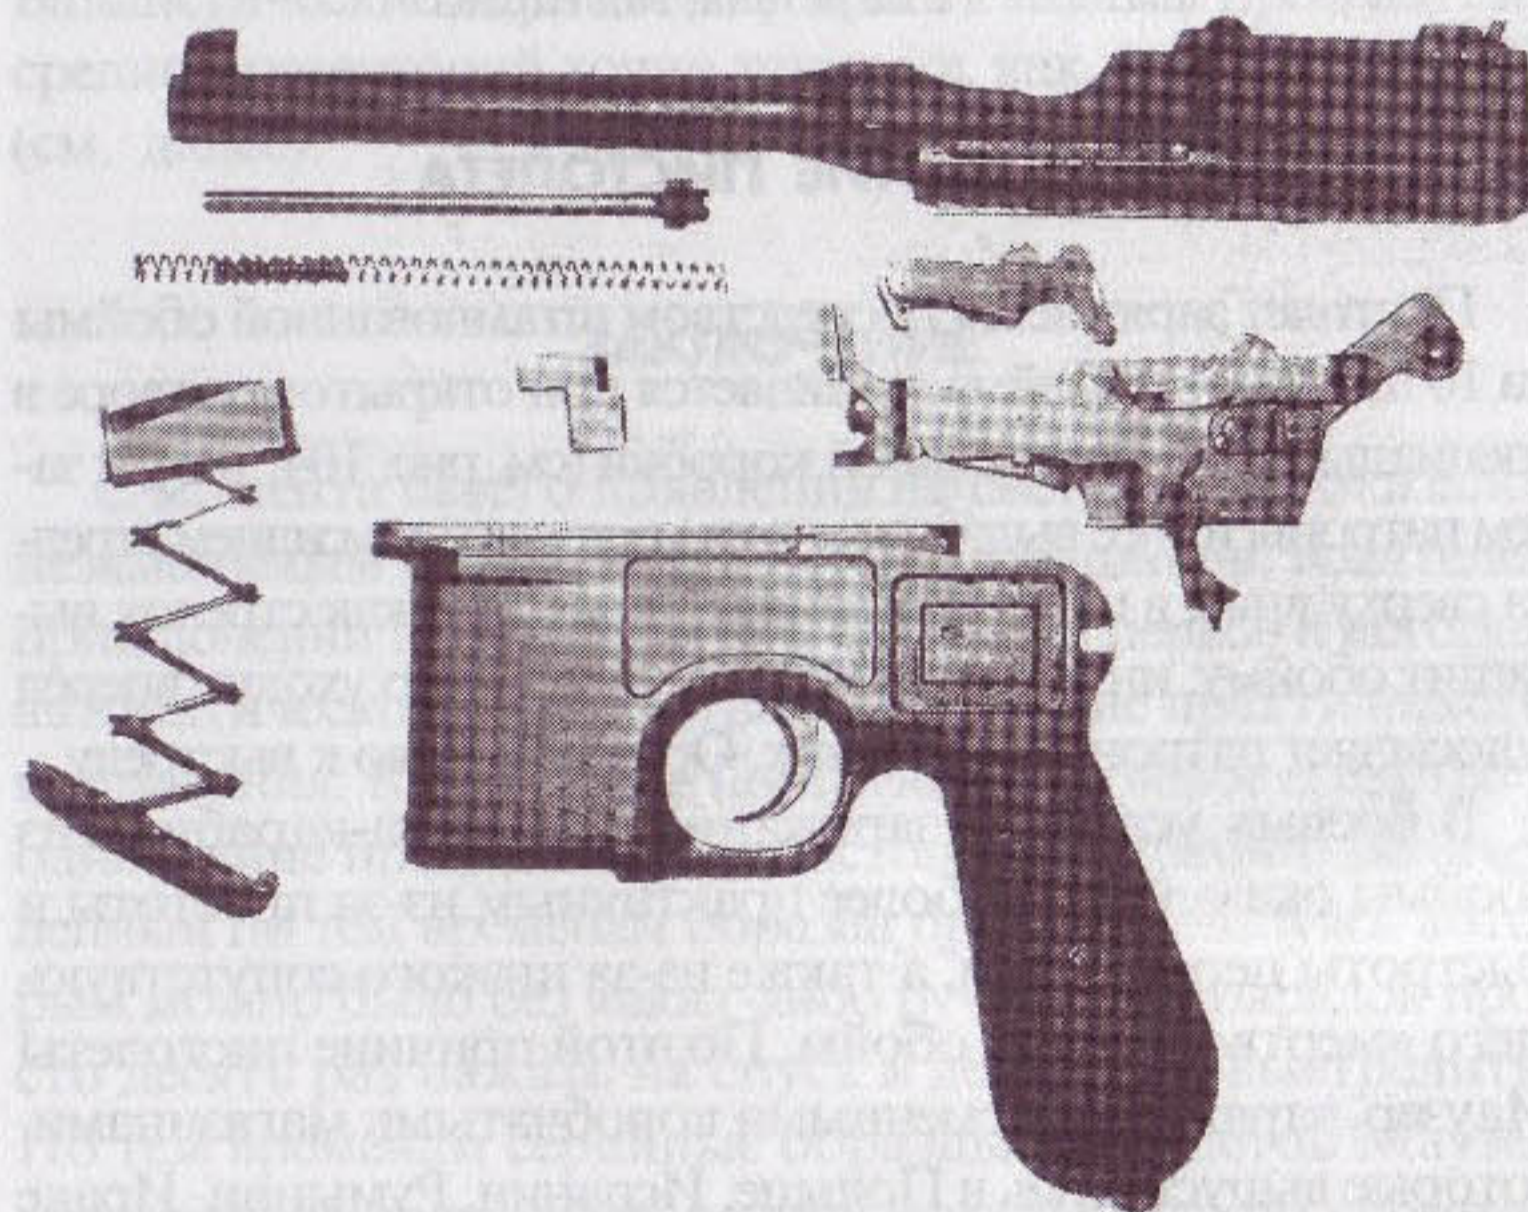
Детали полностью разобранного Маузера 7,63, вид слева
